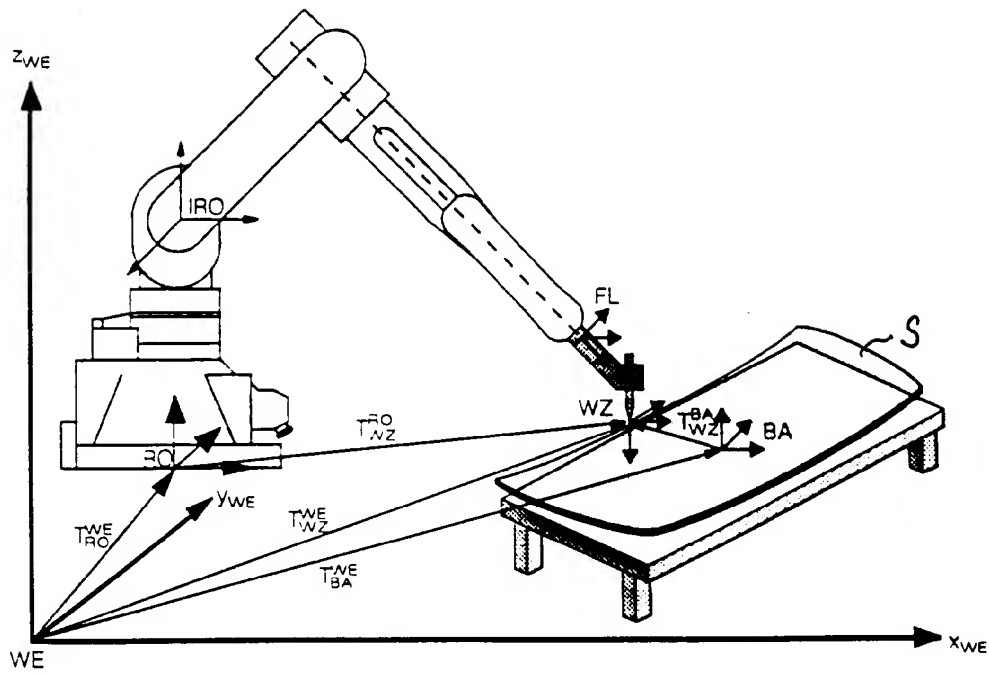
Führung des Werkzeugs über ein ortsfestes Werkstück
